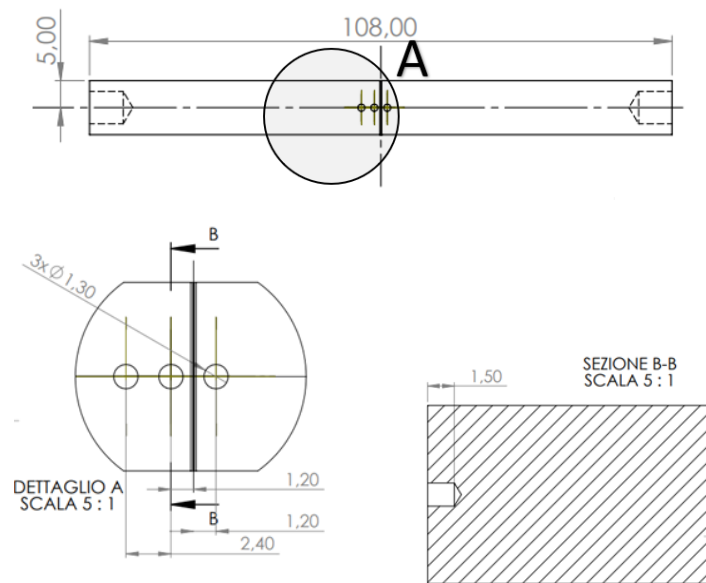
3: Disposizione e geometria dei collegamenti DCPD
